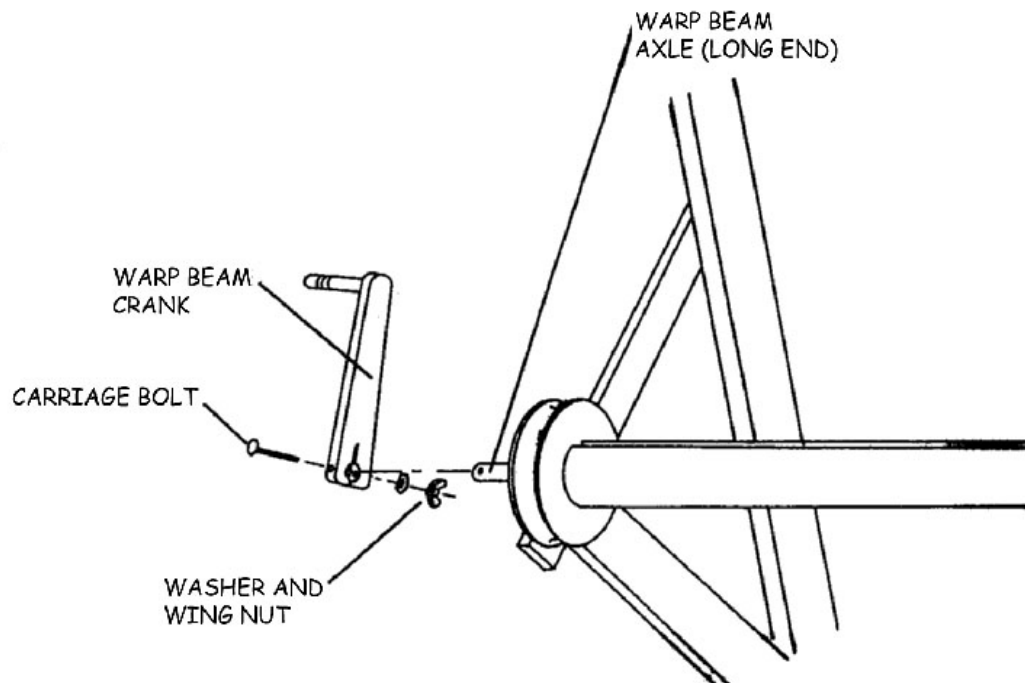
Befestigen Sie die Kettbaumkurbel
